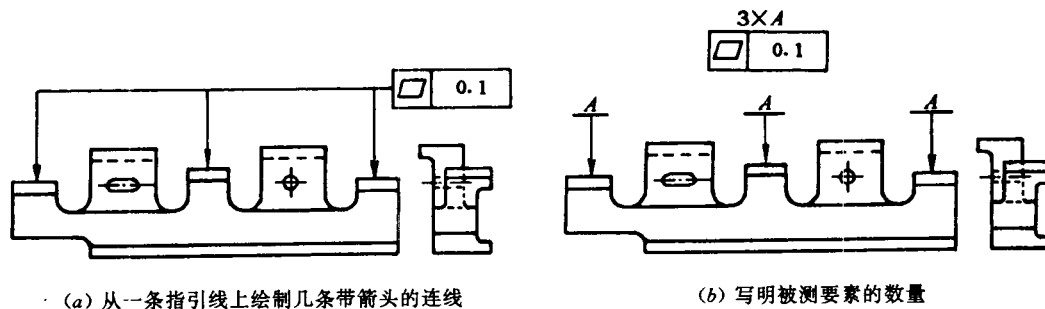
几个被测要素有同一形位公差带要求的简化标注示例
